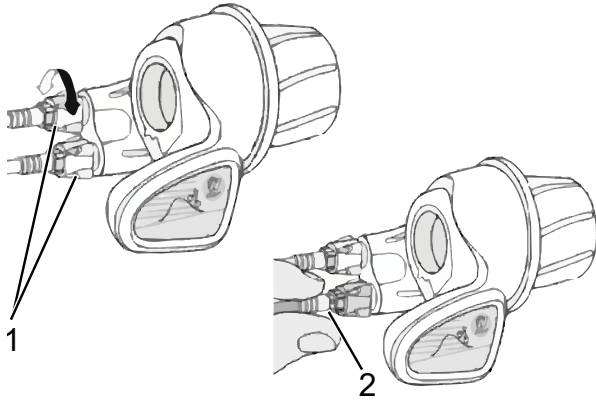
Slutmuffer (2) på to alternative udførelser (A og B) af et gearskift med to kabler på baggaffelen (1)
